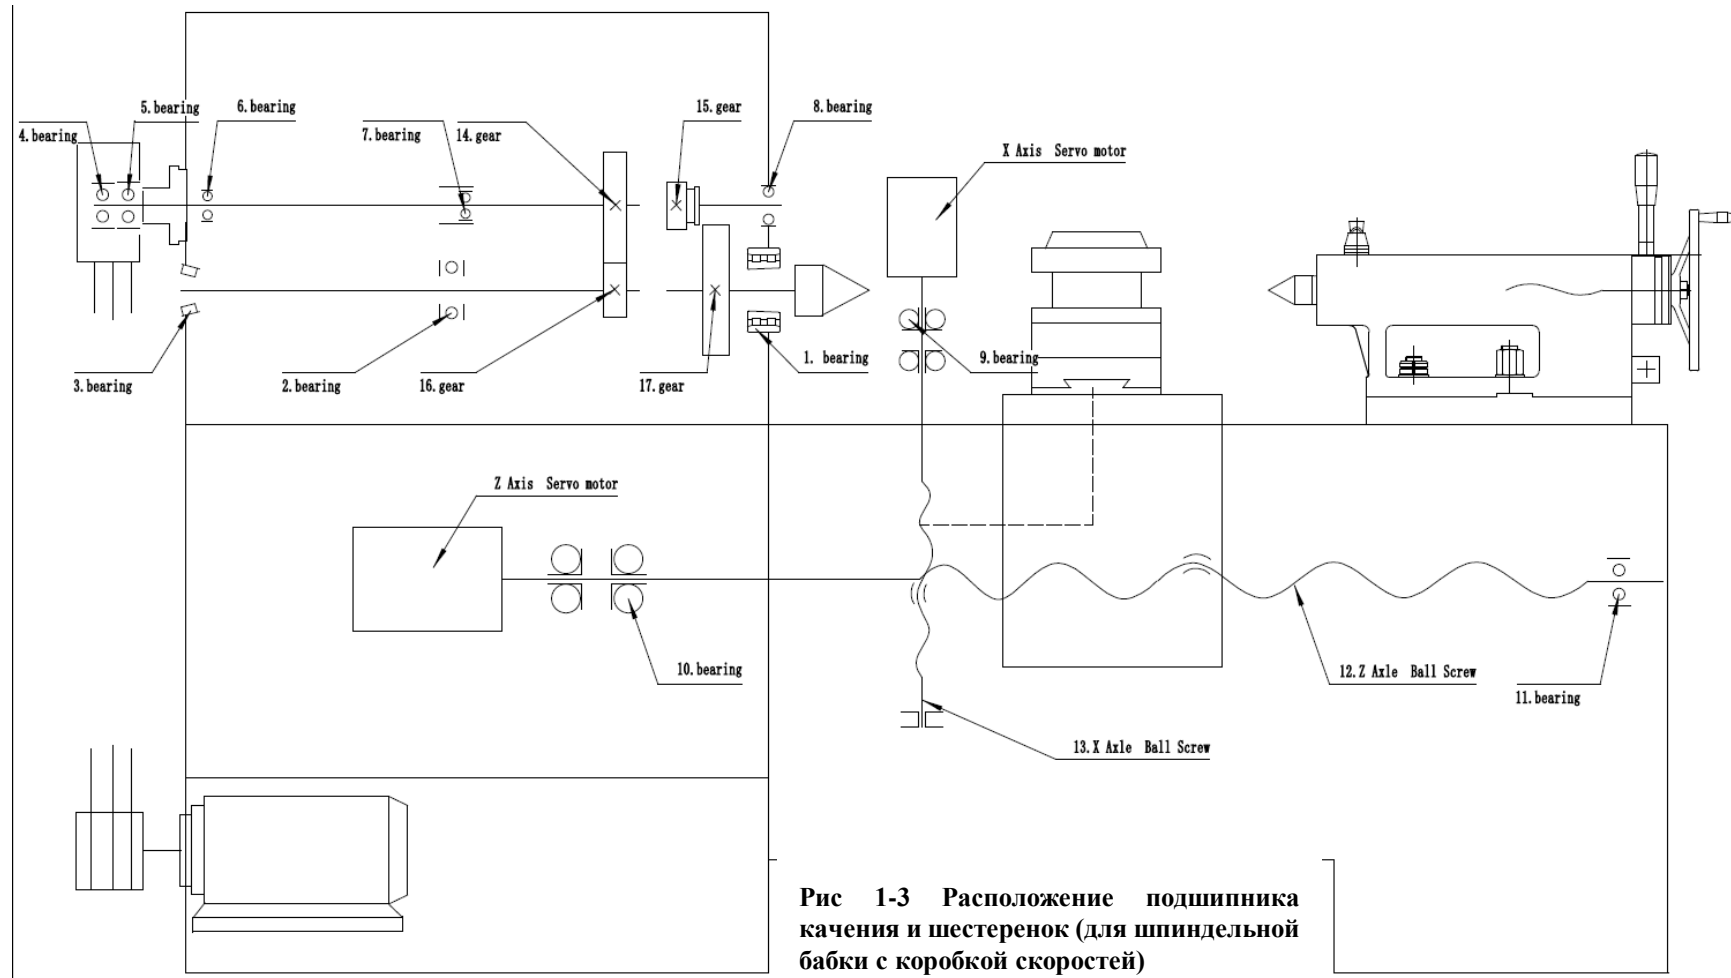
Расположение подшипника качения и шестеренок (для шпиндельной бабки с коробкой скоростей)
